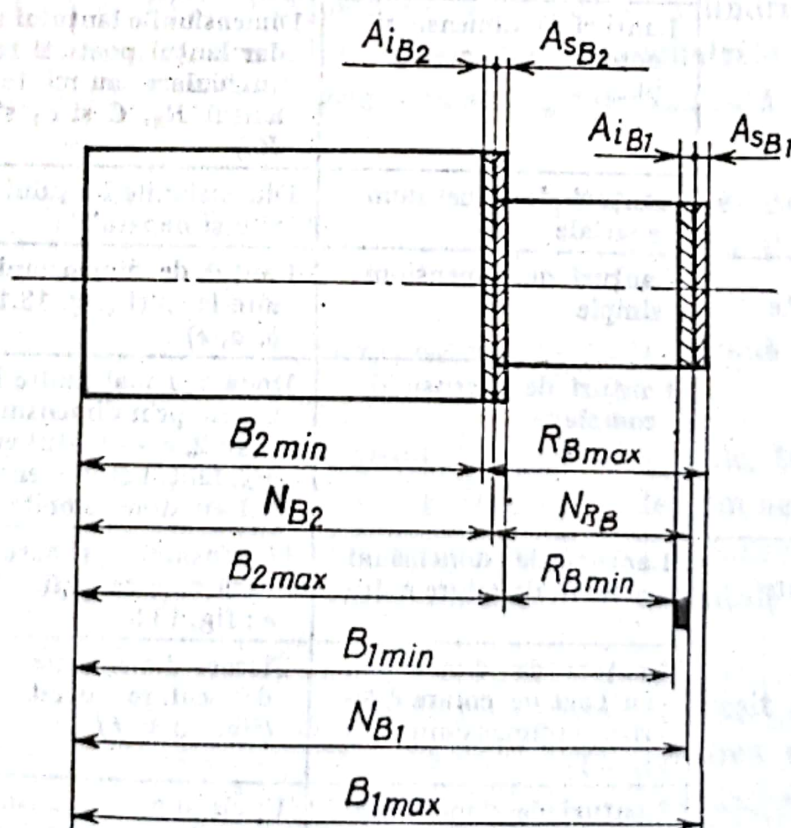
Schemă de rezolvare a lanțurilor de dimensiuni.
